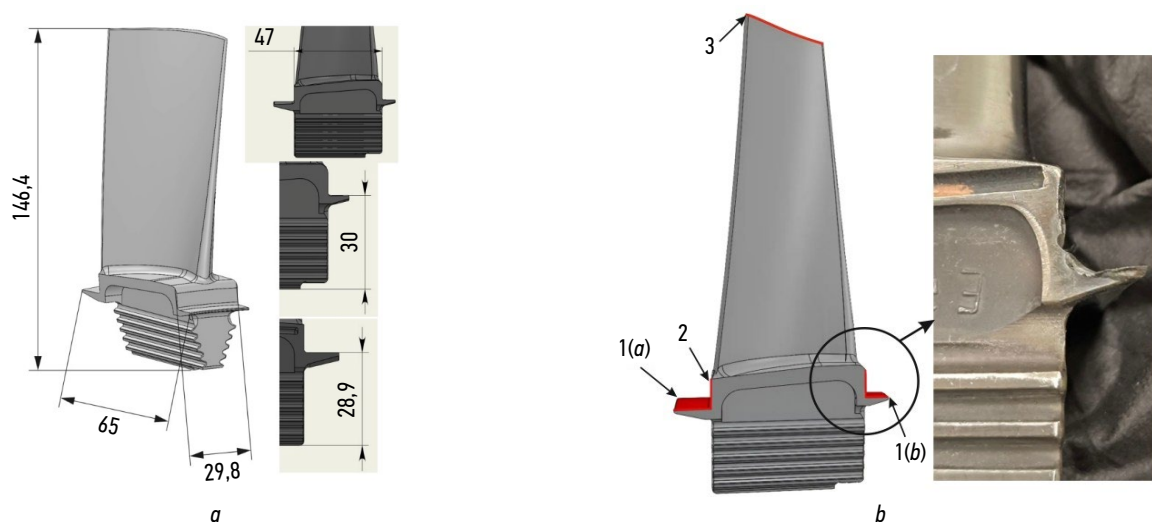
Внешний вид рабочей лопатки ДР-59Л: *a* — размеры рабочей лопатки; *b* — изношенные поверхности рабочей лопатки.
